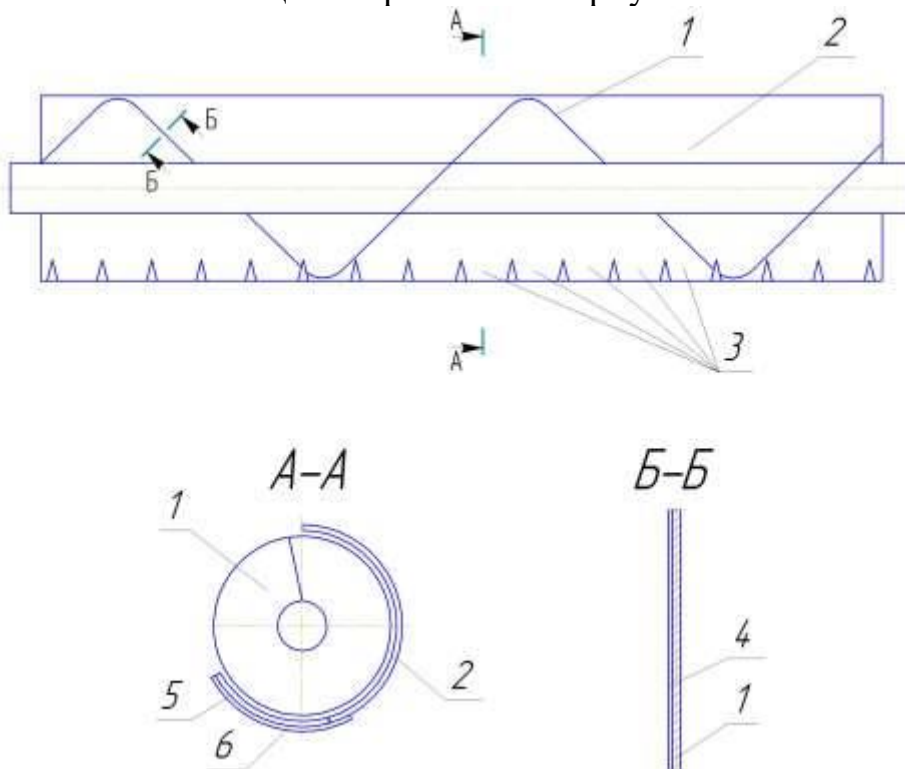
Схема шнекового ріжучого апарату з накладками із фторопласту: 1 – лопаті шнека; 2 – корпус; 3 – вирізи; 4 – накладки з фторопласту; 5 – протиріжучі пластини; 6 – пальці
